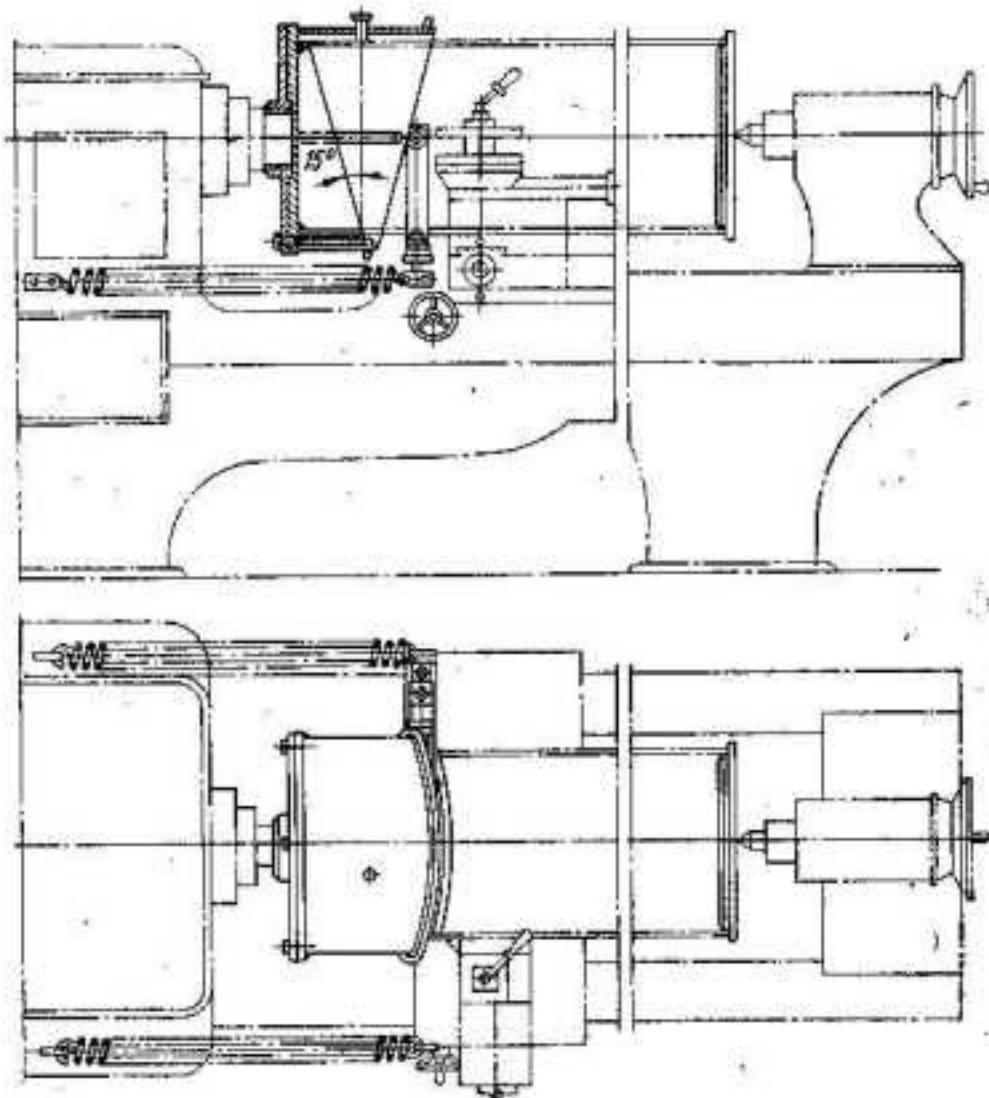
Приспособление для заготовки секторов отводов на токарном станке.
